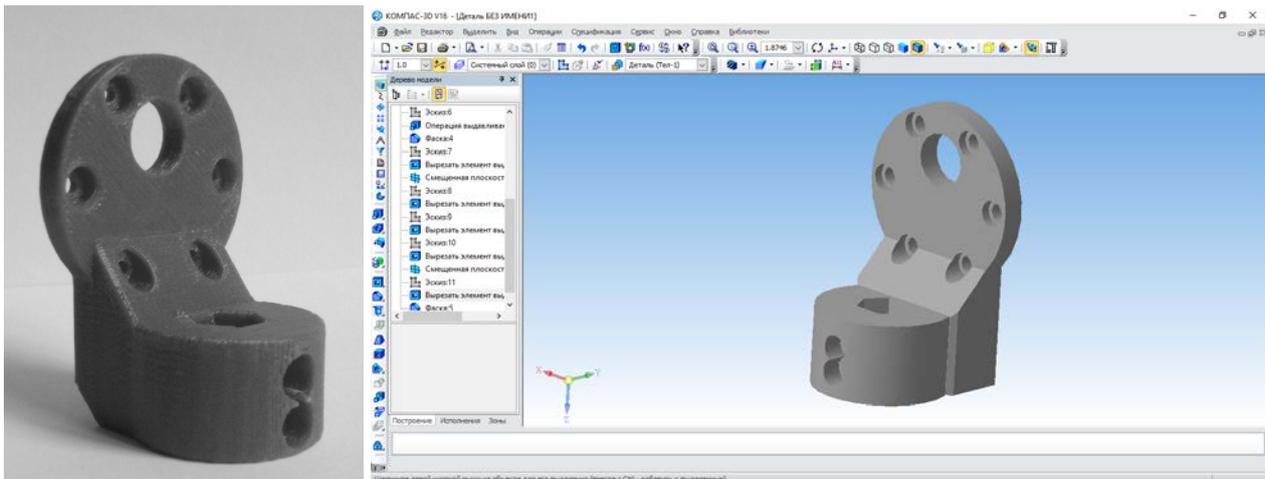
Деталь «Корпус» (а) и 3D-модель детали «Корпус», созданная в КОМПАС-3D (б)
